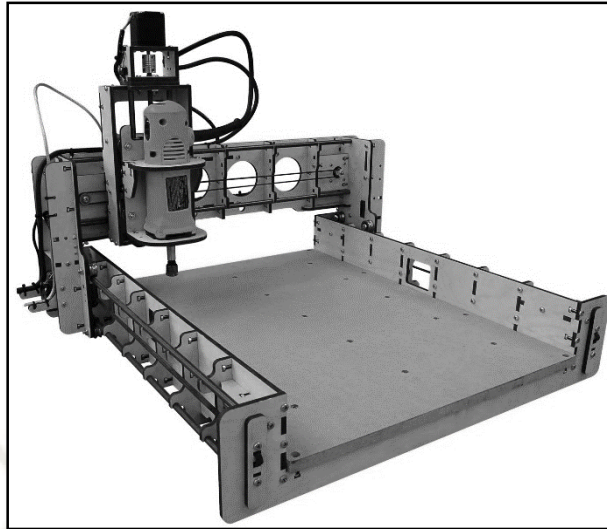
Router CNC 4'x8' Heavy Duty - CNC Machine Kit (greenBull 4X).
